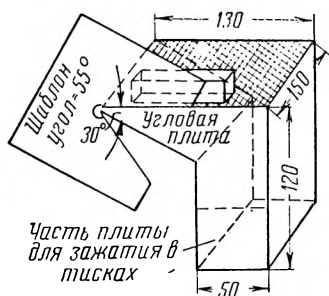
Схема установки шаблона для доводки его внутренней резьбы
